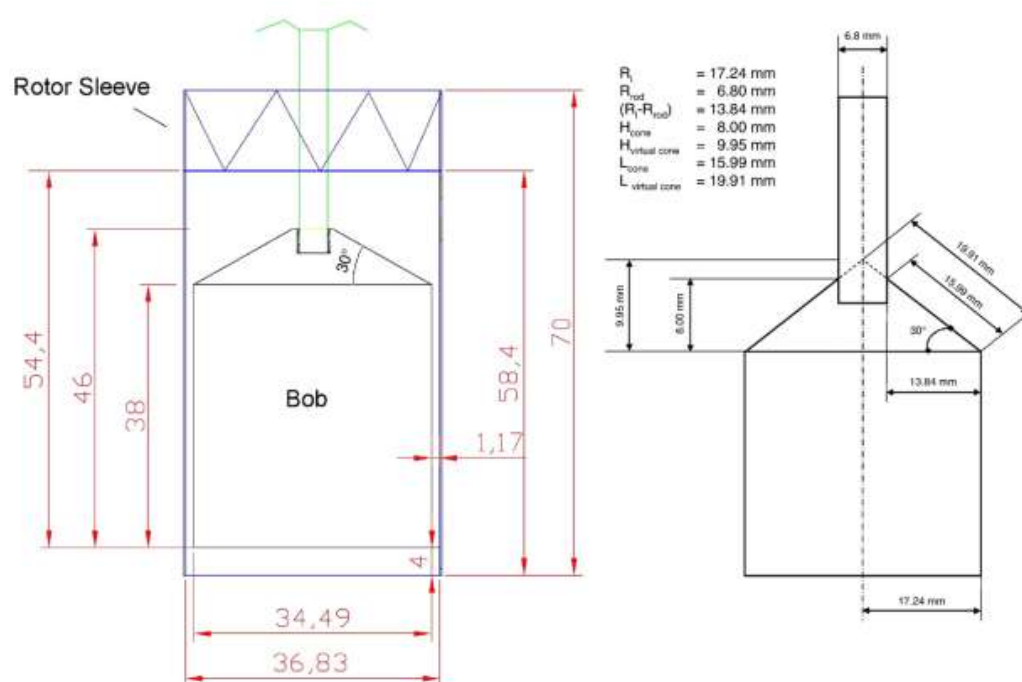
Dimensões do conjunto rotor-bob (11)
